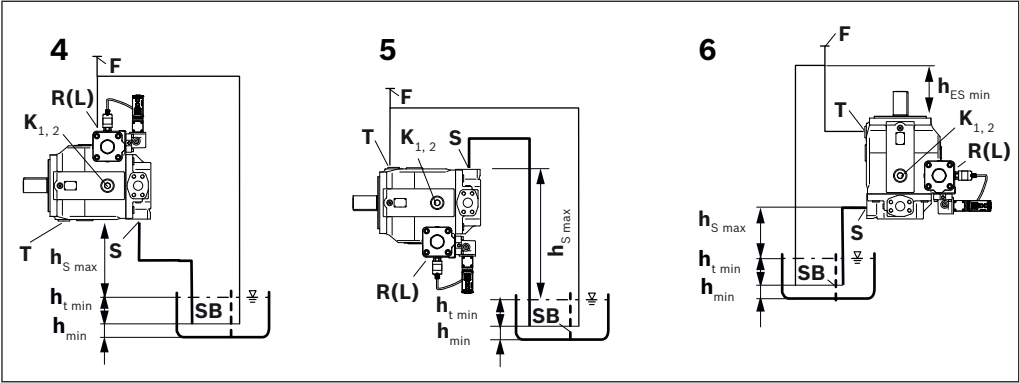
Übertankeinbau A4VSO mit Einbaulage 4–6
